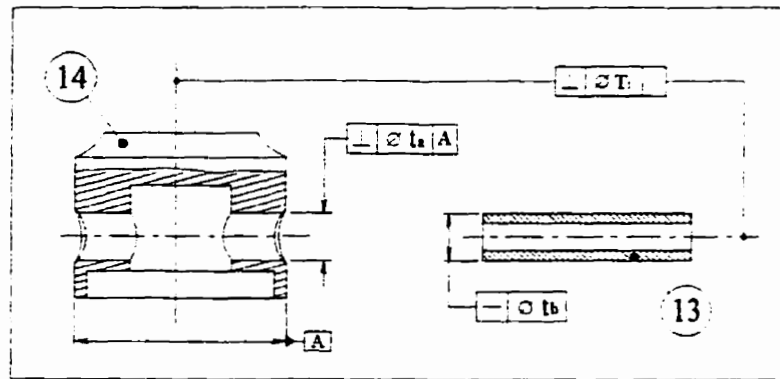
Tolérancement des pièces du groupe piston [1]
